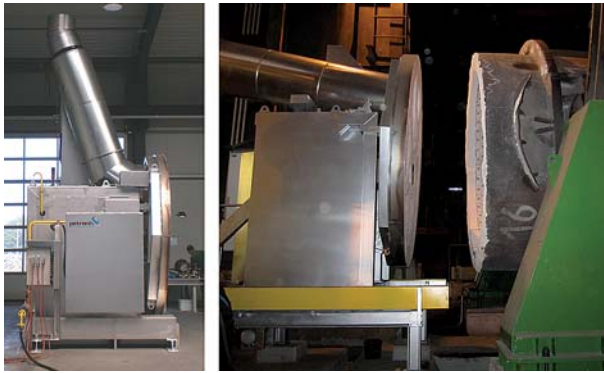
Горизонтальный стенд марки «PETRONIX» для разогрева футеровки сталеразливочных ковшей
